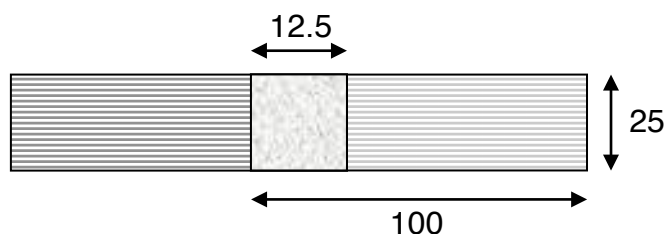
Probeta ensayo tracción para uniones adhesivas a solape simple. Probeta tipo Z1
